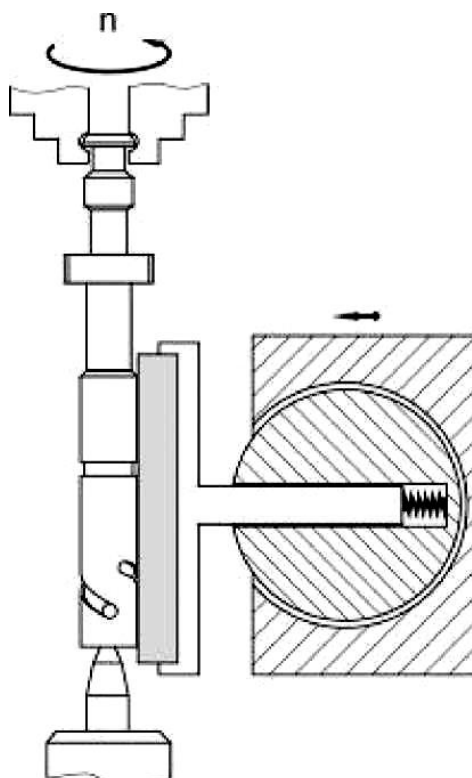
Схема пристрою для шліфування поверхні плунжера
